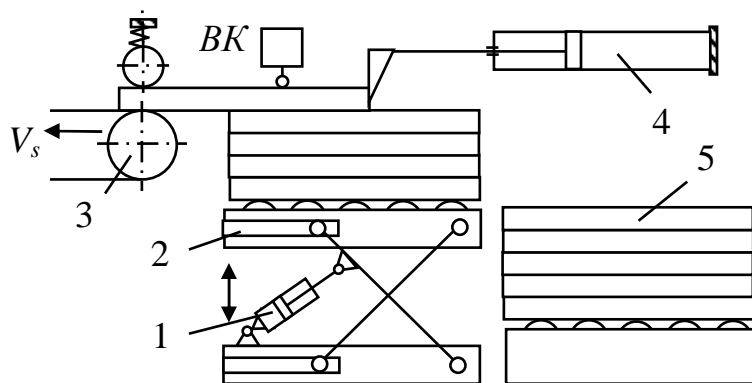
Загрузочно-разгрузочное устройство для щитовых деталей
